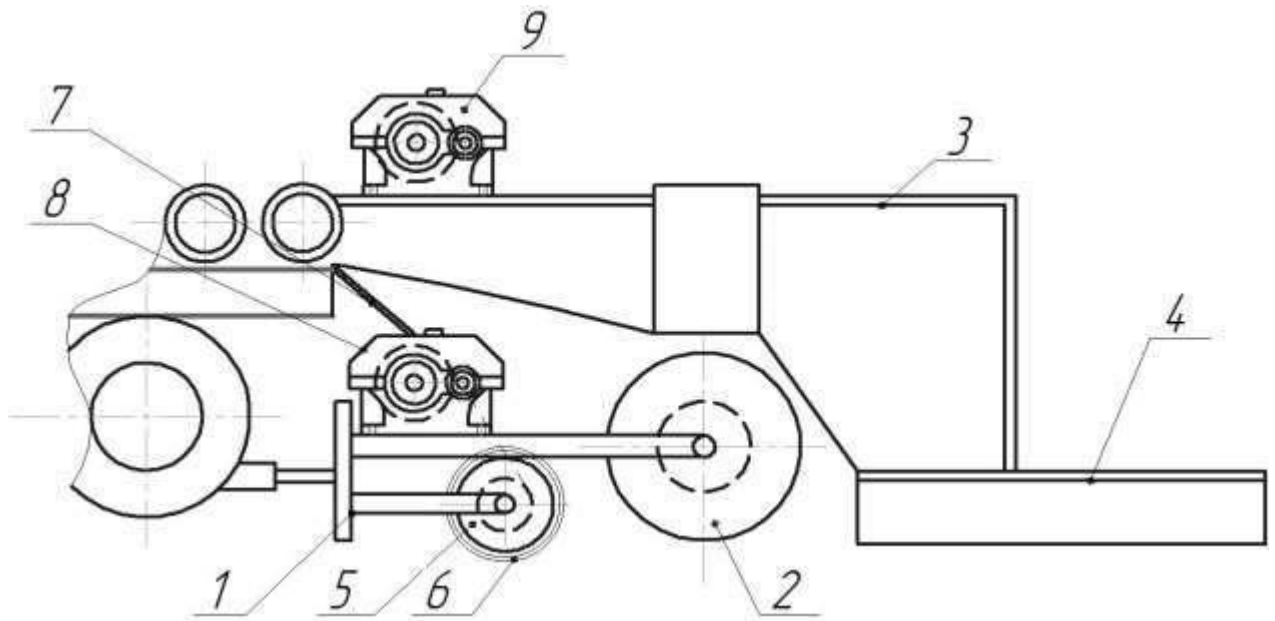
Схема катка-ложеутворювача машини для збирання цибулі-сіянки: 1 – рама; 2 – валець циліндричний; 3 – лоток, що звужує; 4 – валкоутворювач; 5 – валець спіральний; 6 - спіраль; 7 – лоток сходження домішок; 8, 9 – гідро двигун.
